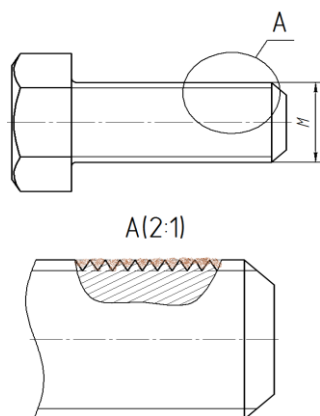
Щели, образованные на резьбовой части болта
